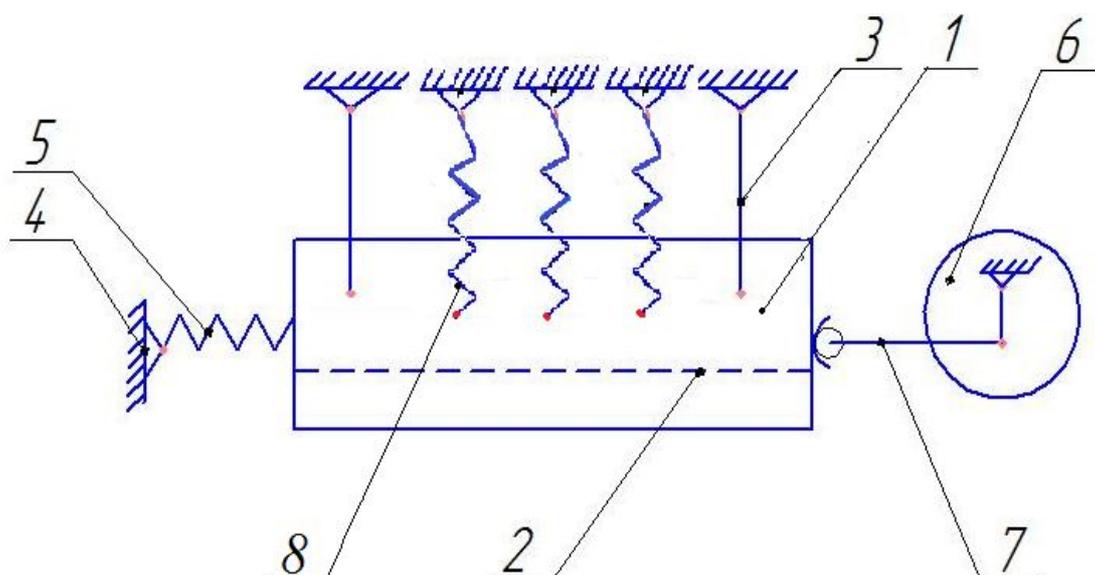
Схема подвеса решетного стана: 1 – решетный стан; 2 – решетка; 3 – подвеска; 4 – корпус машины; 5 – пружина; 6 – эксцентрик; 7 – толкатель; 8 – цилиндрические витые пружины
